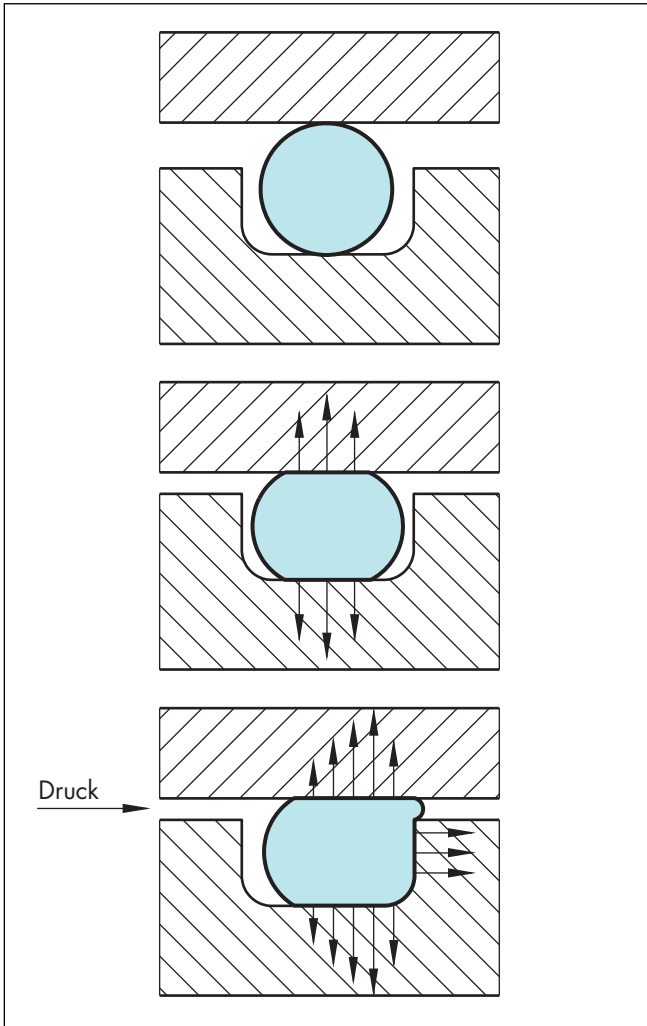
O-Ring Anpresskräfte mit und ohne Systemdruck
